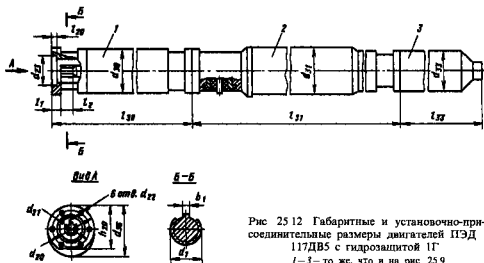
12 Габаритные и установочно-при- соединительные размеры двигателей ПЭД 117ДВ5 с гидрозащитой ПГ 1—3 — то же, что и на рис 25 9
